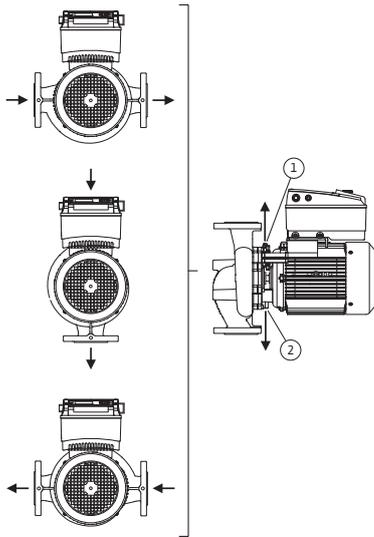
Positions de montage autorisées avec arbre moteur horizontal
